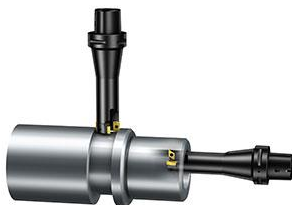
Токарська обробка зовнішньої і внутрішньої поверхонь на багатоцільовому верстаті різцем однієї конструкції
